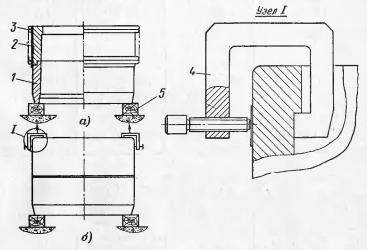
Разборка составного бандажного кольца. a-установка кольца; 6- приспособление для разъединення; 1- кольцо; 2- кольцо; 3- нндуктор; 4-струбцина; 5- выкладка шпальная.
